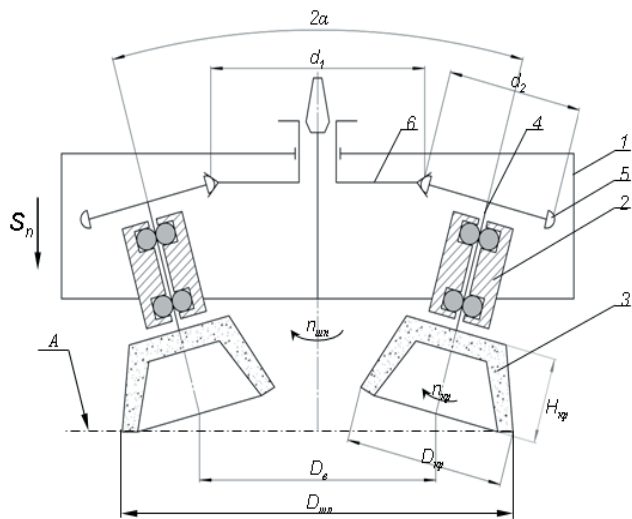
Конструктивно-компоновочная схема торцевой планетарно-шлифовальной головки
